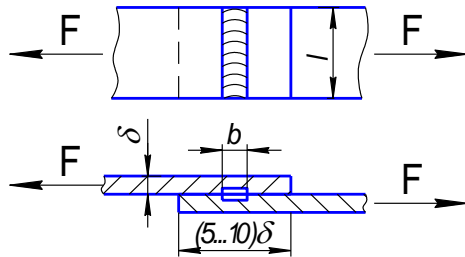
Розрахункова схема з'єднання, що виконане шовним зварюванням
